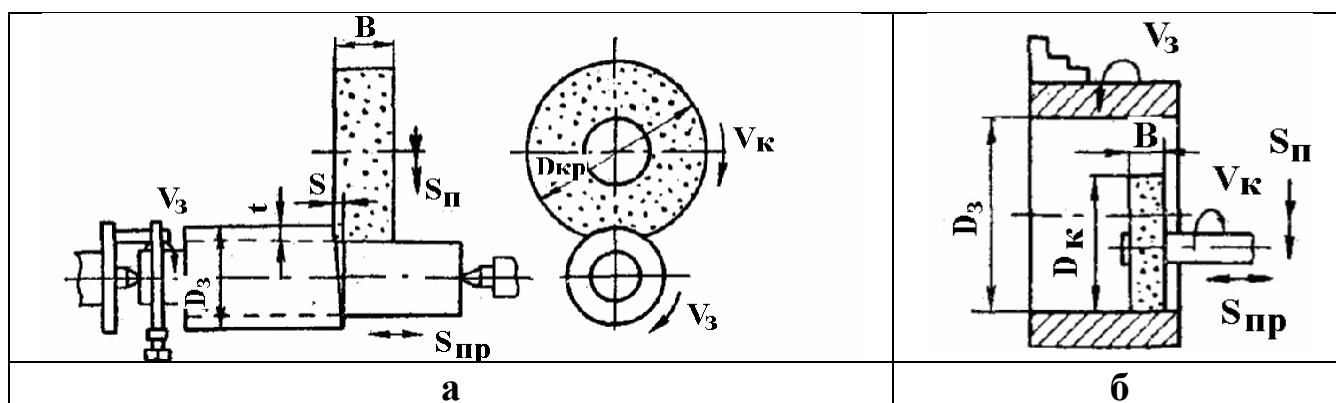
Типовые схемы обработки на шлифовальных станках:
